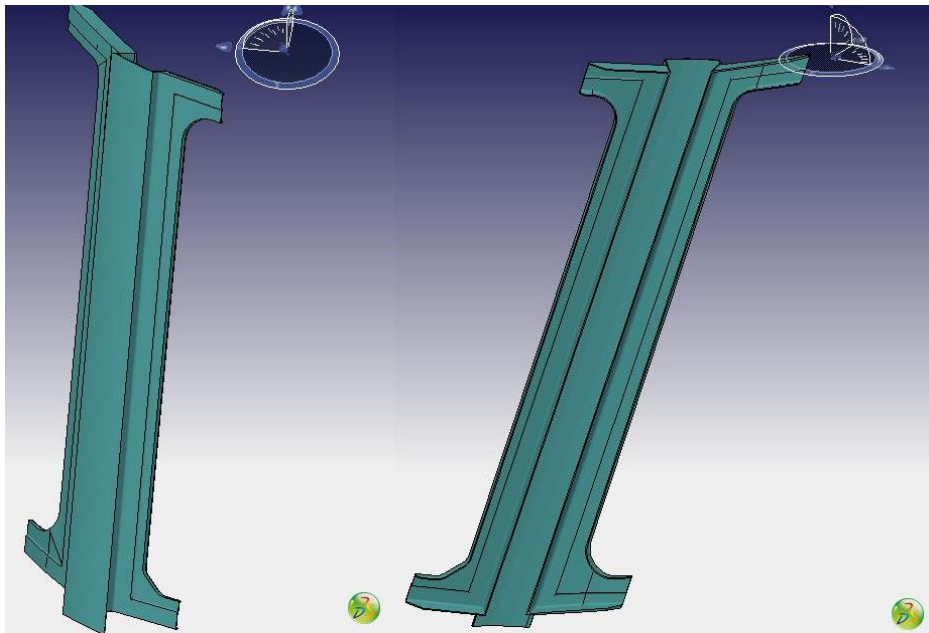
Proposta de alteração da viga lateral da estrutura.
